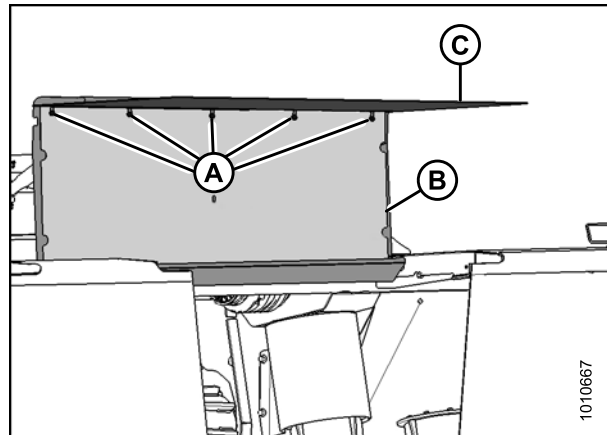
Écrous fixant le panneau de blindage et le rideau à la porte de la barre de coupe
